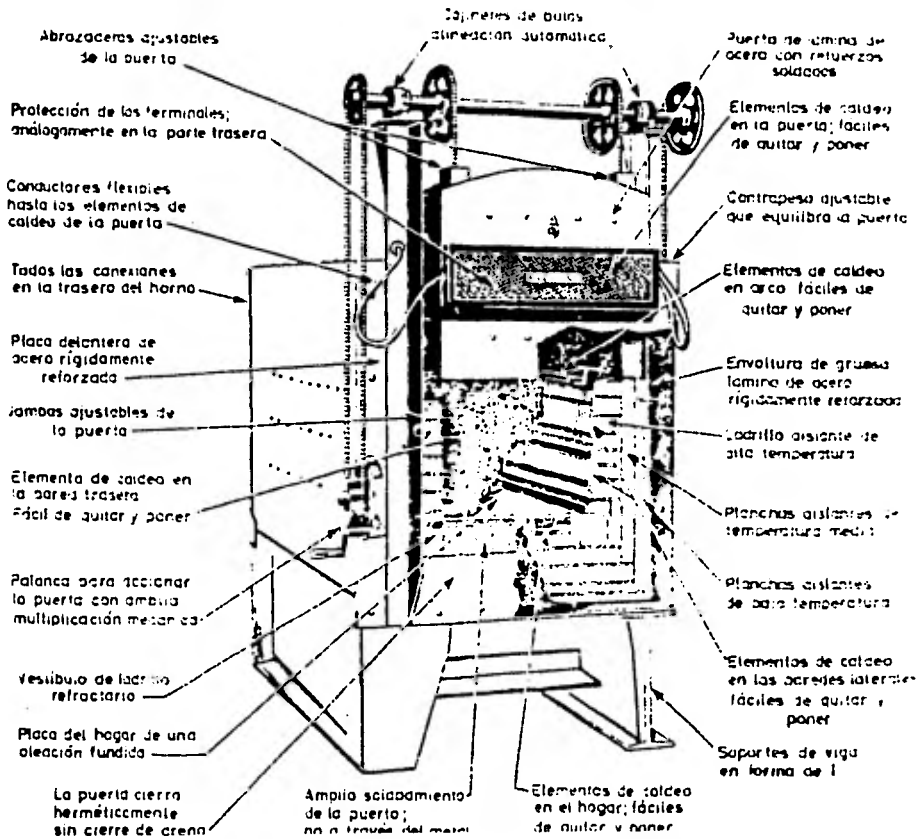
Horno para liberación de tensiones generadas por la soldadura.
